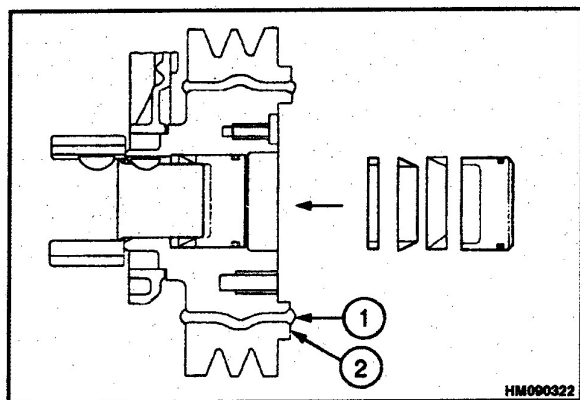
Установка шкива коленчатого вала, двигателя типа YG и YH.
